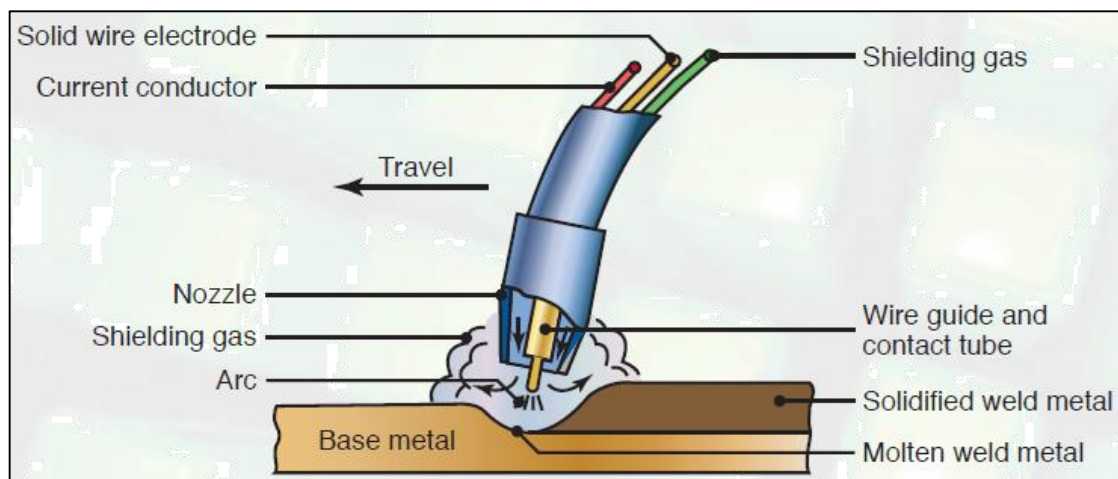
esquematización de soldadura por sistema MIG.
